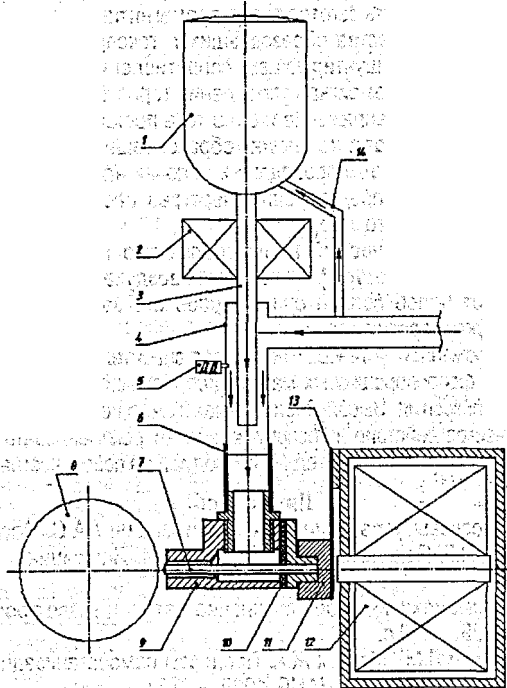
Установка для нанесения ферропорошковых покрытий:
